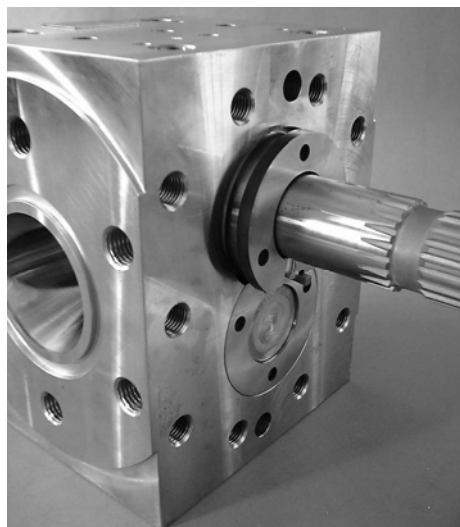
Монтаж подшипника скольжения стороны привода сверху
